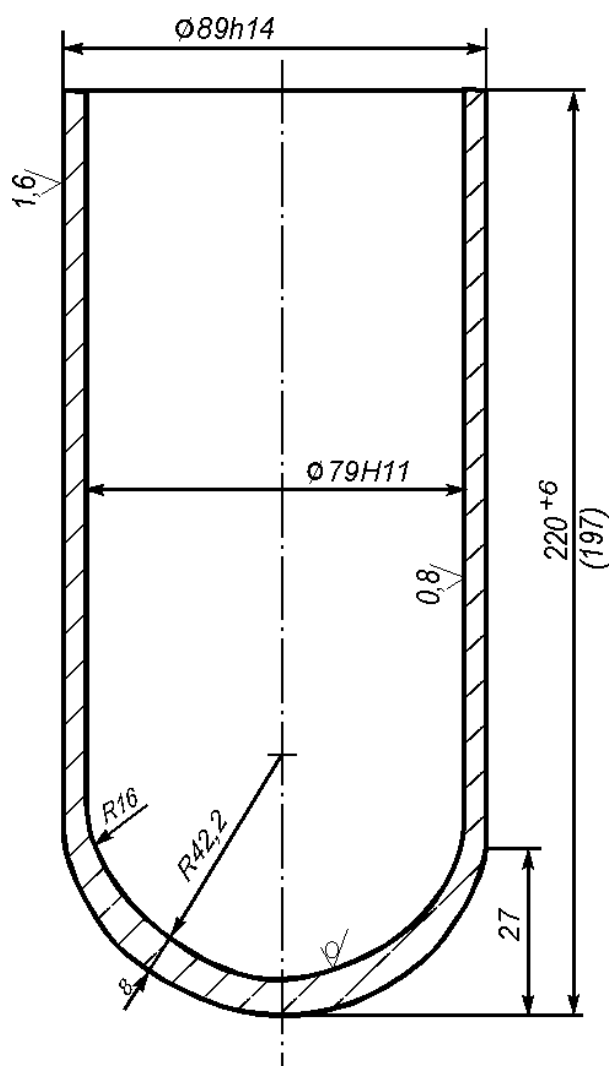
Штампована заготовка циліндра приводу засувки
